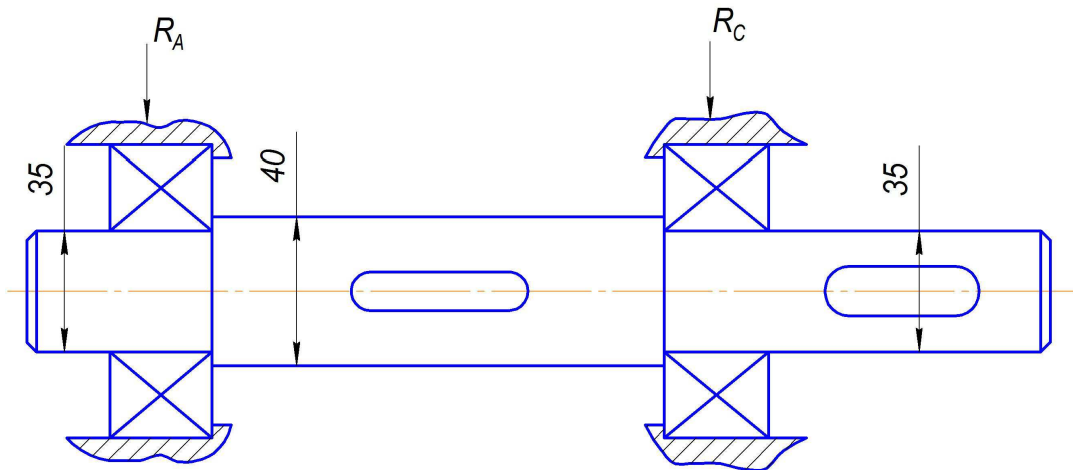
Схема до вибору підшипників для проміжного вала
